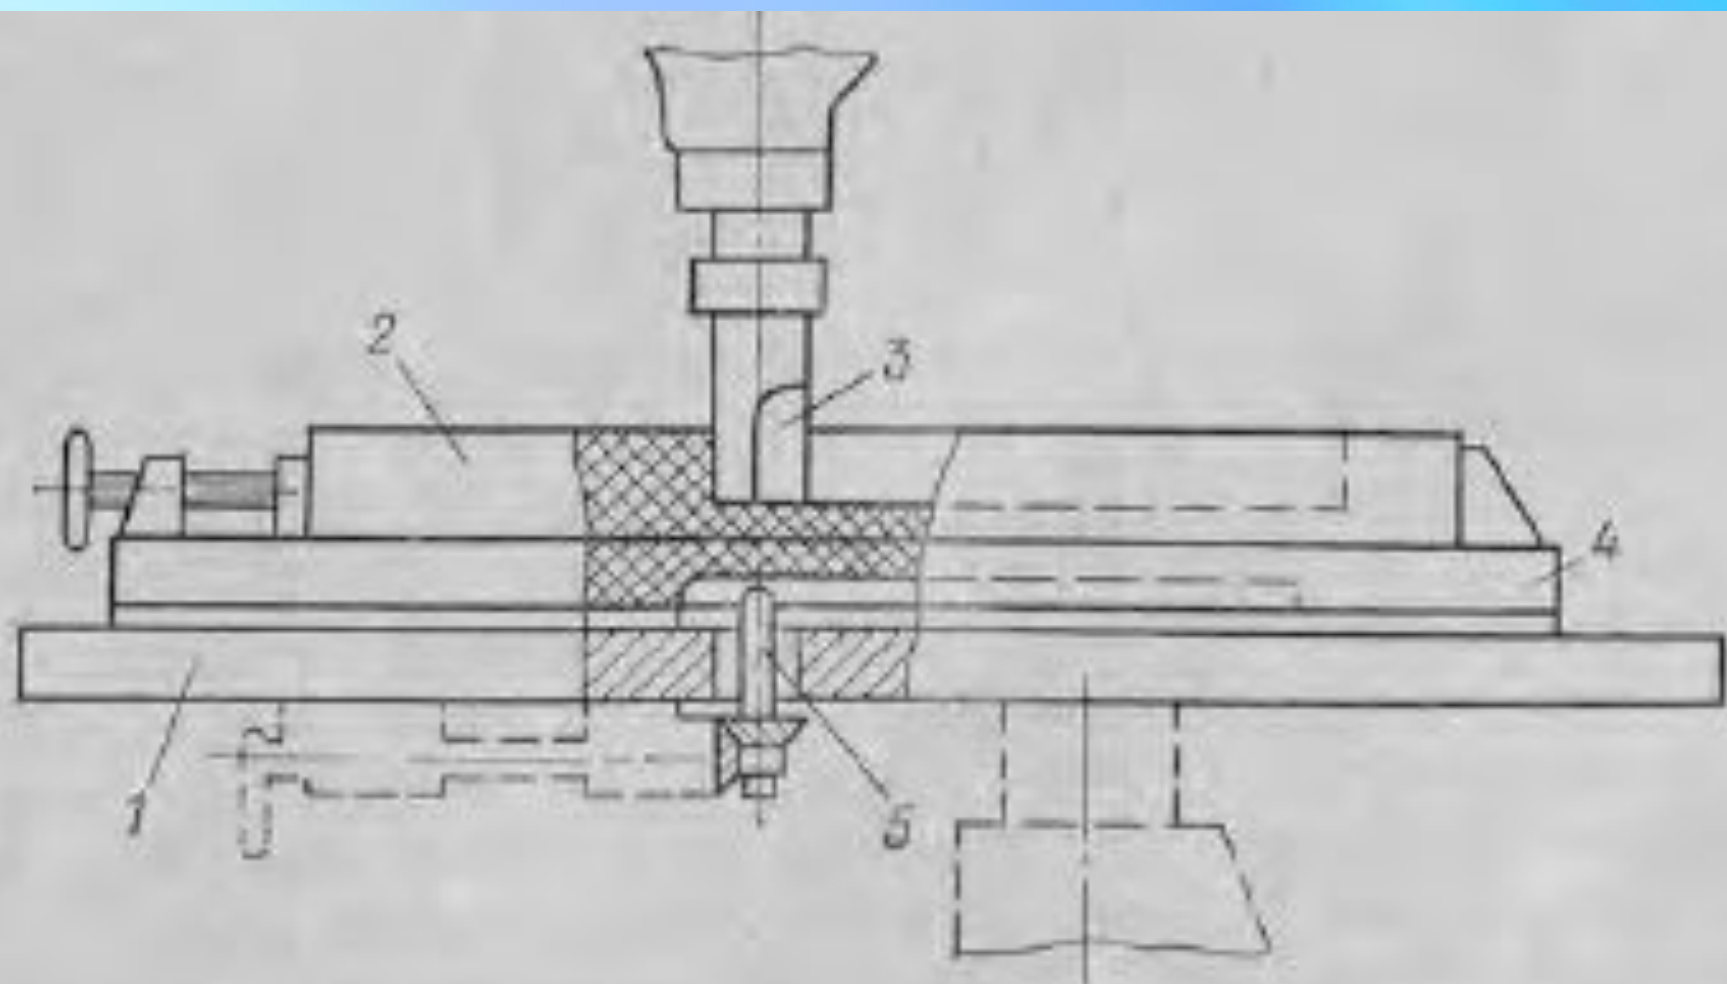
Схема фрезерования на копировально-фрезерном станке
